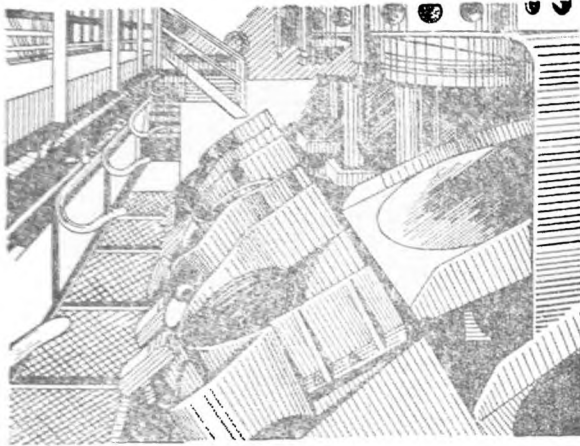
Опрокидывающийся стул для навешивания мотков проволоки на крюки конвейера
